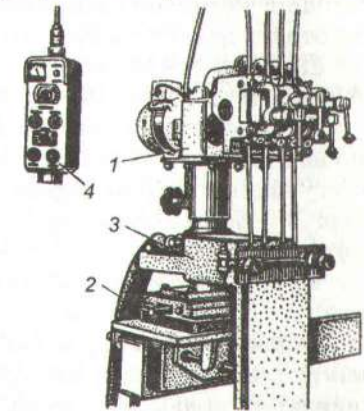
Апарат А-1304 для електрошлакового зварювання плавким мундштуком:
